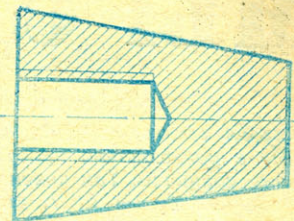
Схема переходного конуса (резьбовая часть — под вал двигателя, конусная — под патрон дрели).
